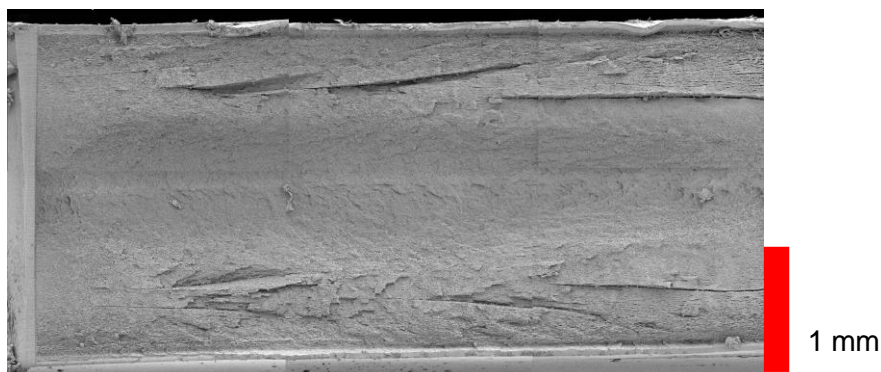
Imatge composta de la superfície de fractura de Bioblend 0 zona lateral
